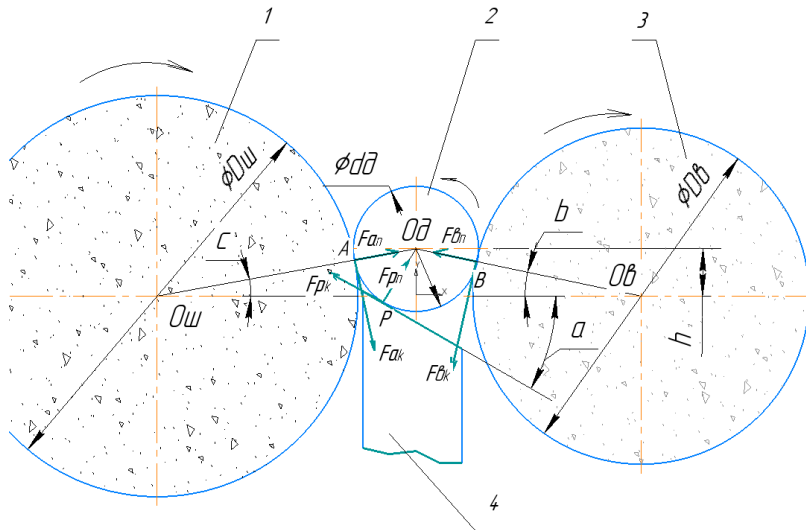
Схема сил при проходном бесцентровом шлифовании (центры осей кругов расположены на горизонтальной прямой): 1 – шлифовальный круг; 2 – обрабатываемая деталь; 3 – ведущий круг; 4 – опорный нож
